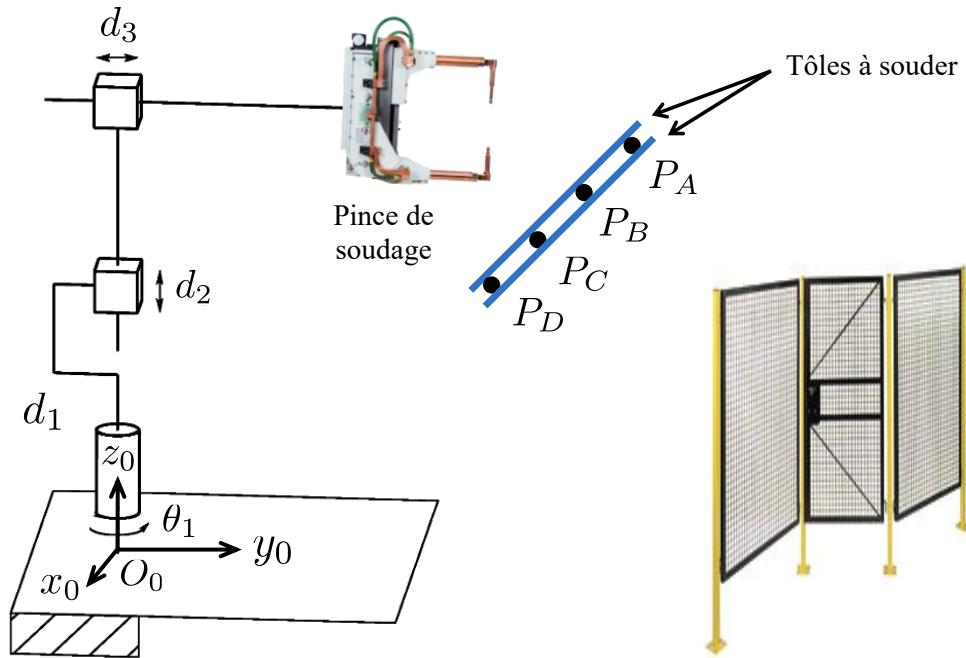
Manipulateur cylindrique dans une cellule de soudage.
